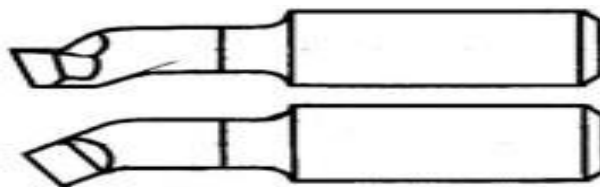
Резец 2140– 0523 ГОСТ 18872– 73
